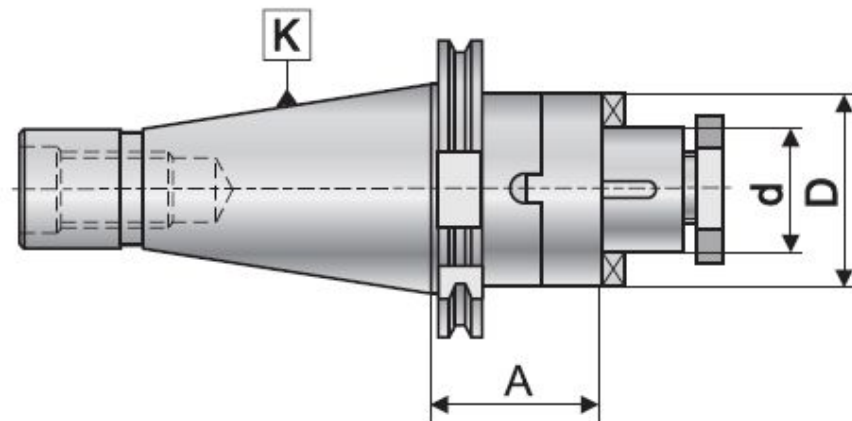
Общий вид системы вспомогательных инструментов для сверлильных и фрезерных станков с ЧПУ
